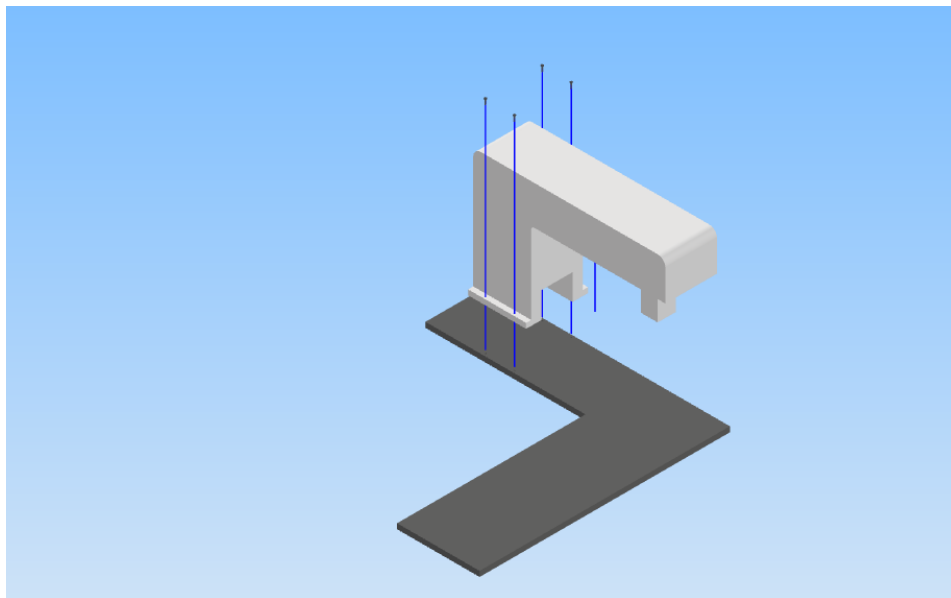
Vista explosionada del ensamblaje mostrado en la figura 3.58.
